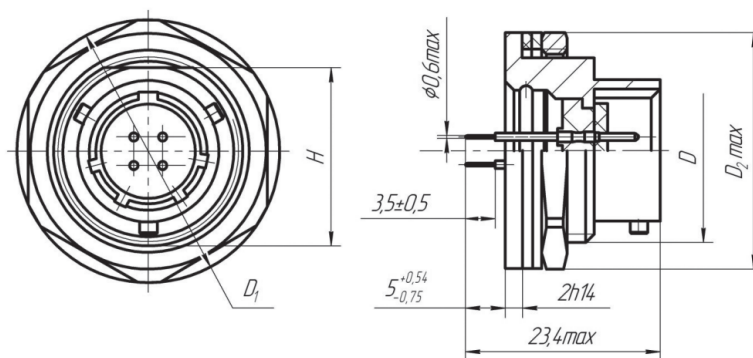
Габаритные размеры вилки приборной ОНЦ-БС
